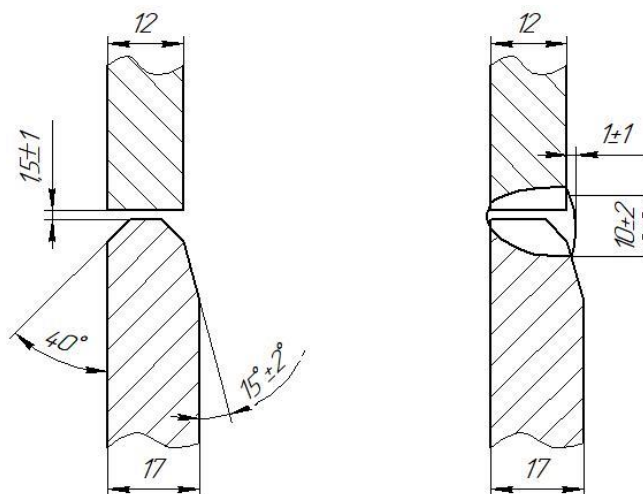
Форма подготовки кромок и форма сварного шва при выполнении кольцевого шва при соединении фланца отвода
